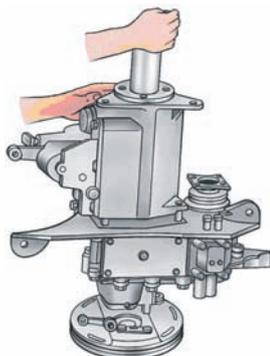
З'єднання коробки передач з роздаточною коробкою
